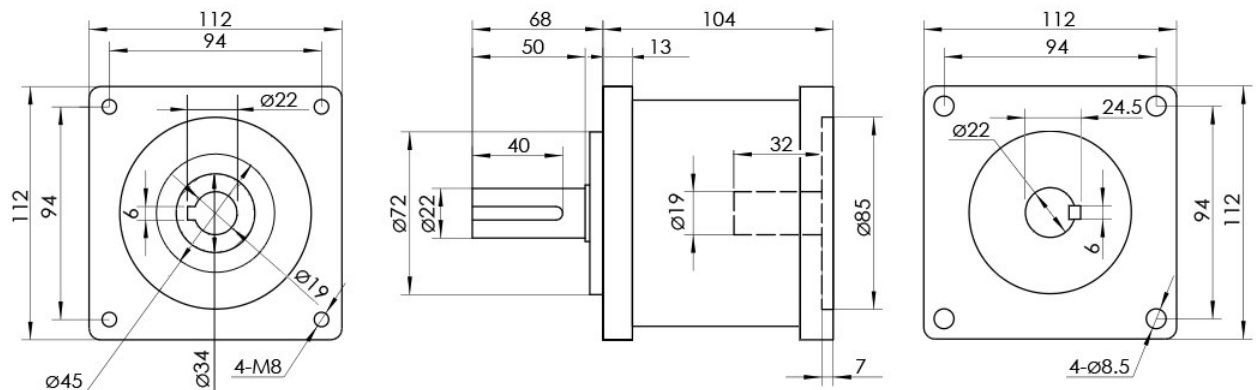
Креслення редуктора планетарного PX110N010SO
